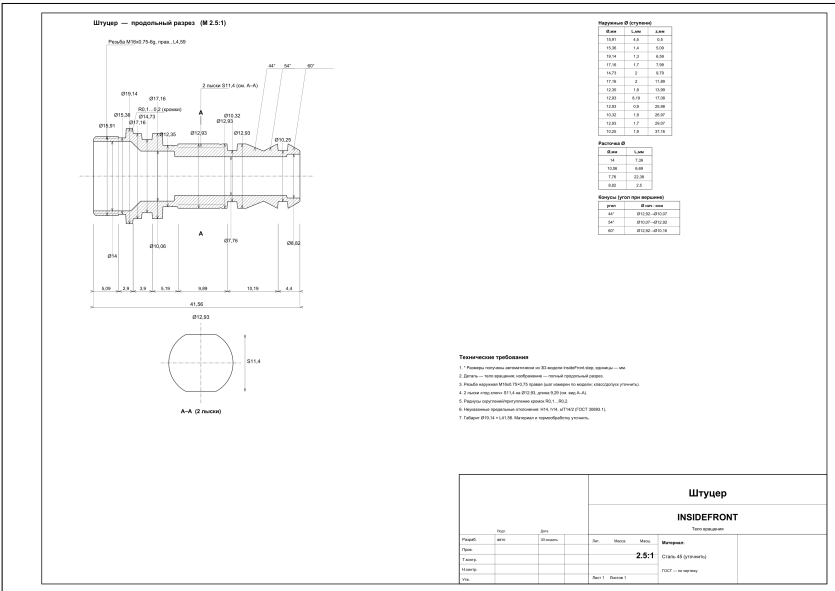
Общий вид чертежа (полный лист — в приложении insideFront_drawing).
